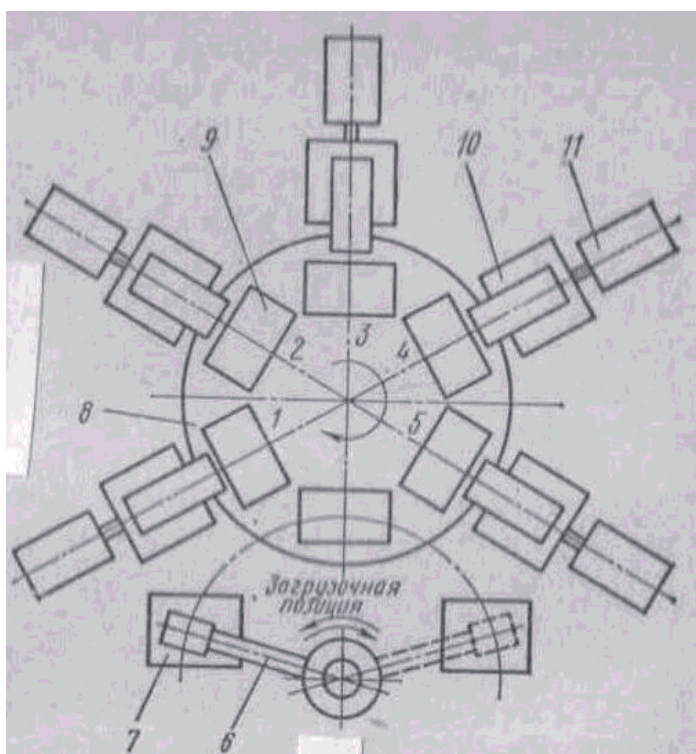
Многопозиционный сборочный автомат: 1 – 5 – сборочные позиции; 6 – манипулятор; 7 – установочная позиция; 8 – поворотный стол; 9 – приспособления на позициях; 10 – сборочные головки; 11 – магазины для комплектующих деталей
